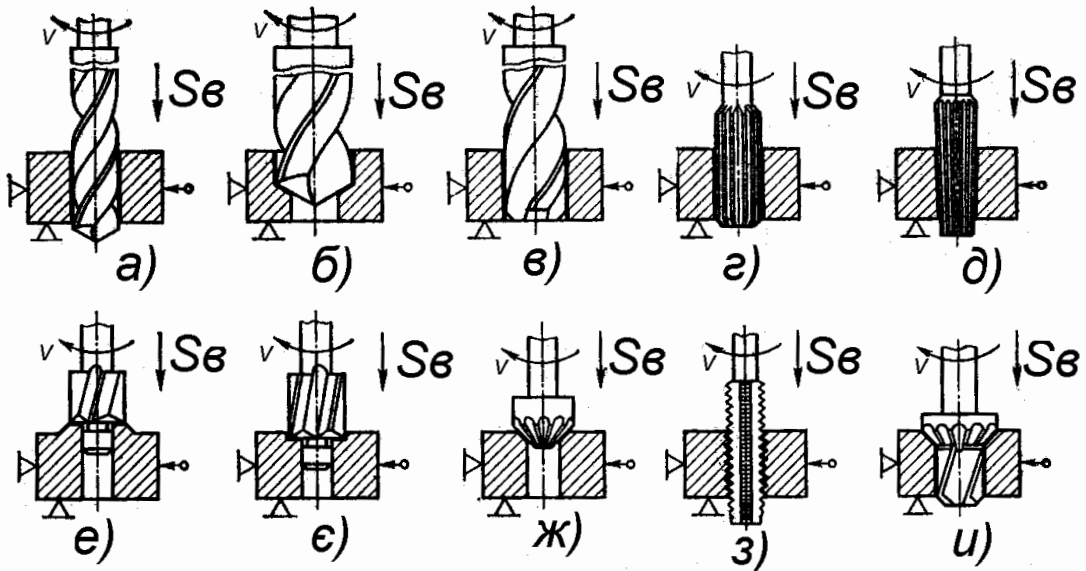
Схеми обробки заготовок на свердильних верстатах
